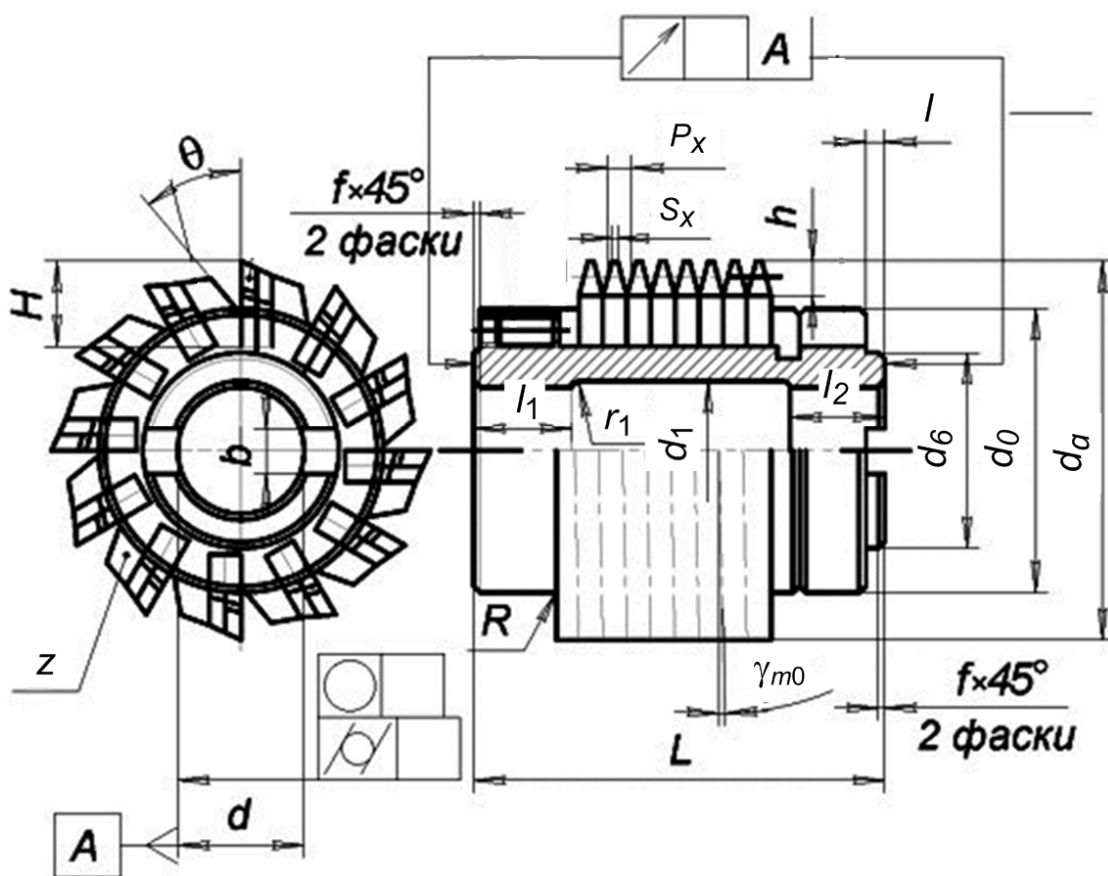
Збірна твердосплавна черв'ячна зуборізальна фреза
